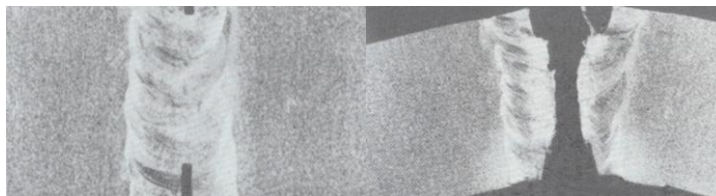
焊缝金属的“刻槽断裂”试验
